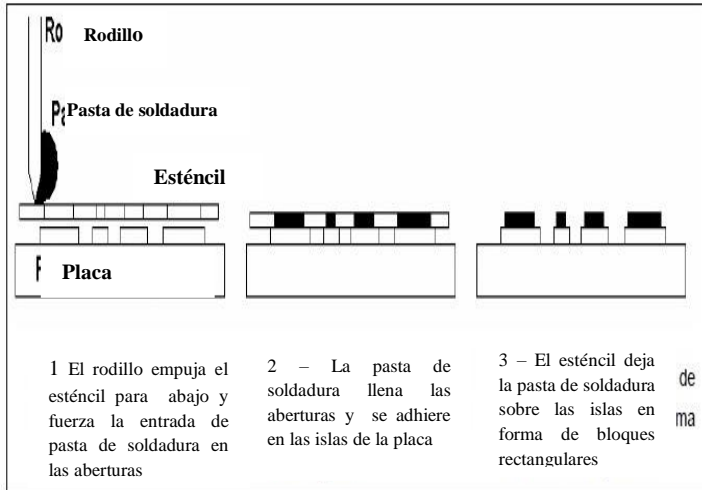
Proceso de deposición de la pasta de soldadura [8].
